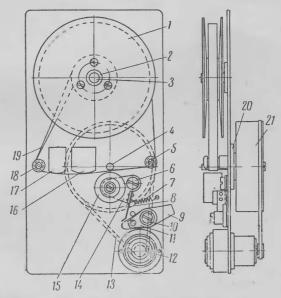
Внешний вид лентопротяжного механизма портативного диктофона с кольцевой лентой.
